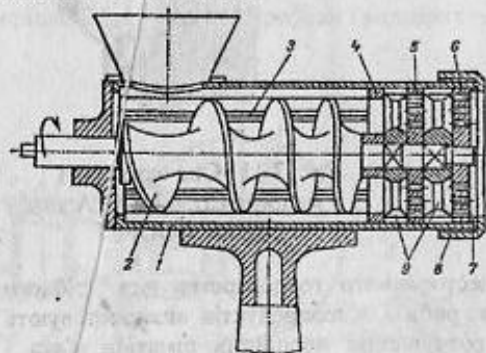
Принципова схема м'ясорубки: 1 – робоча камера; 2 – шнек; 3 – ребра; 4 – решітка підрізна; 5, 6 – решітки ножові; 7 – кільце упорне; 8 – гайка натискна; 9 – ножі
